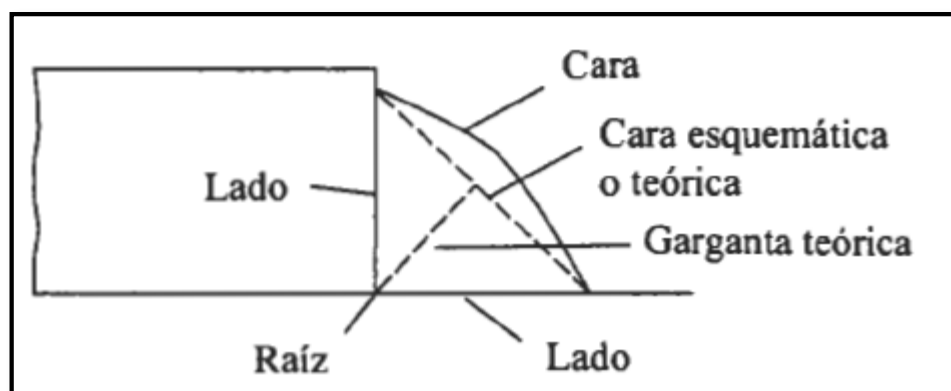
Esquema de soldadura de filete (McCormac J. C., 2002)
